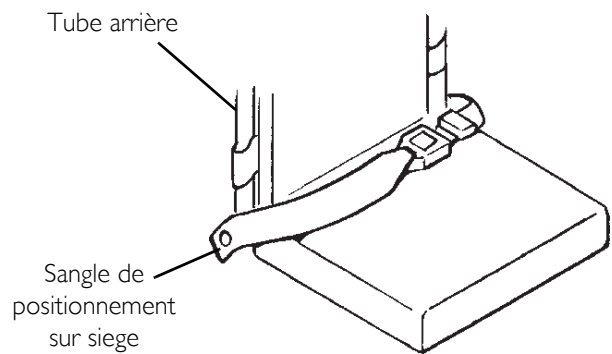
Installation de la sangle de positionnement sur le siège
